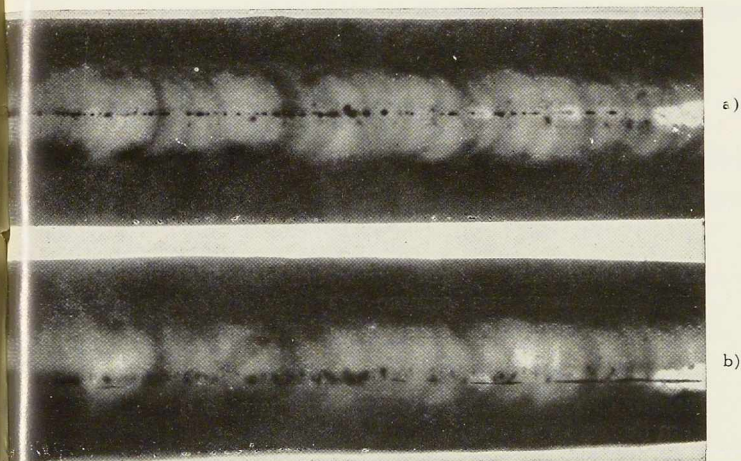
Soudure au chalumeau sur de l'acier coulé de 10 mm, soudure en U. Inclusions de scories et défauts de soudure.
